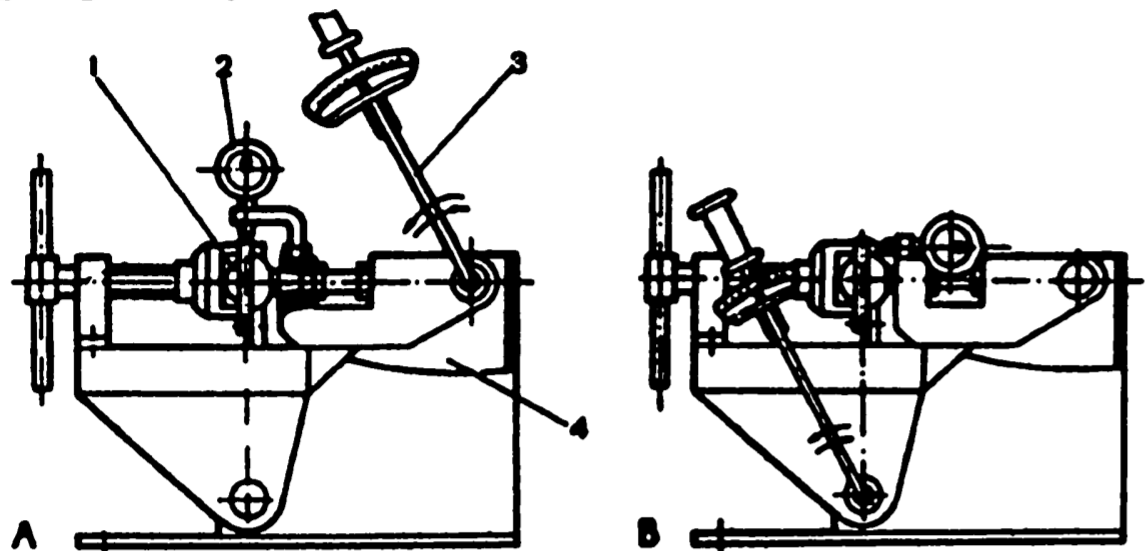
Проверка верхнего шарового шарнира на приспособлении 02.8701.9502: 1 - шаровой шарнир; 2 - индикатор; 3 - динамометрический ключ; 4 - приспособление 02.8701.9502; А - схема проверки радиального зазора; В - схема проверки осевого зазора
